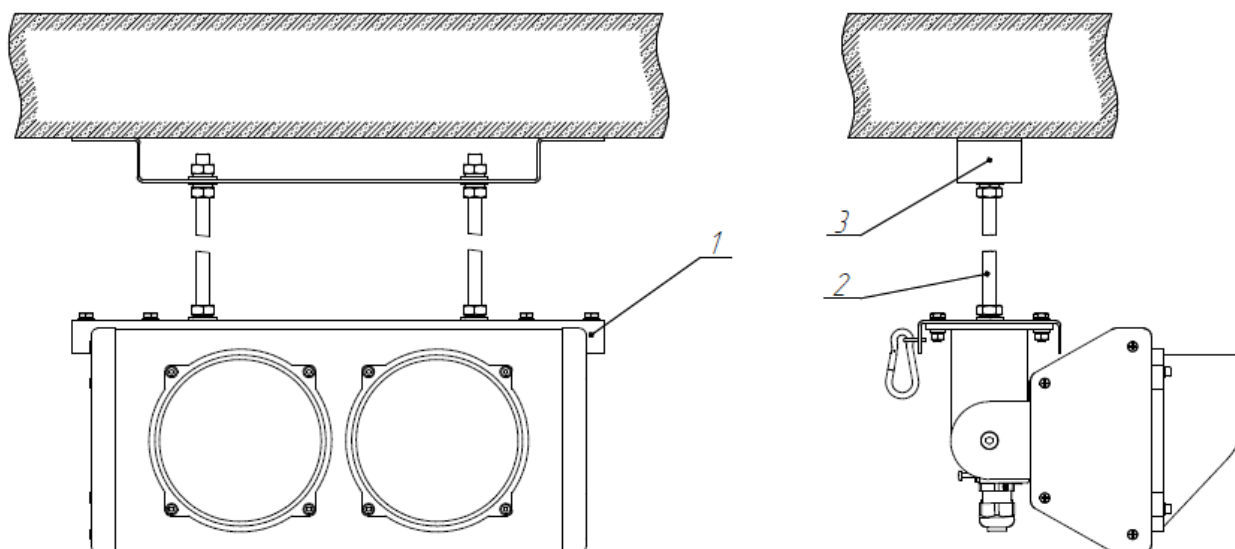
установка БСР с использованием комплекта крепления светофора ТИС 34.1.1.18.000 к кровле выработки
